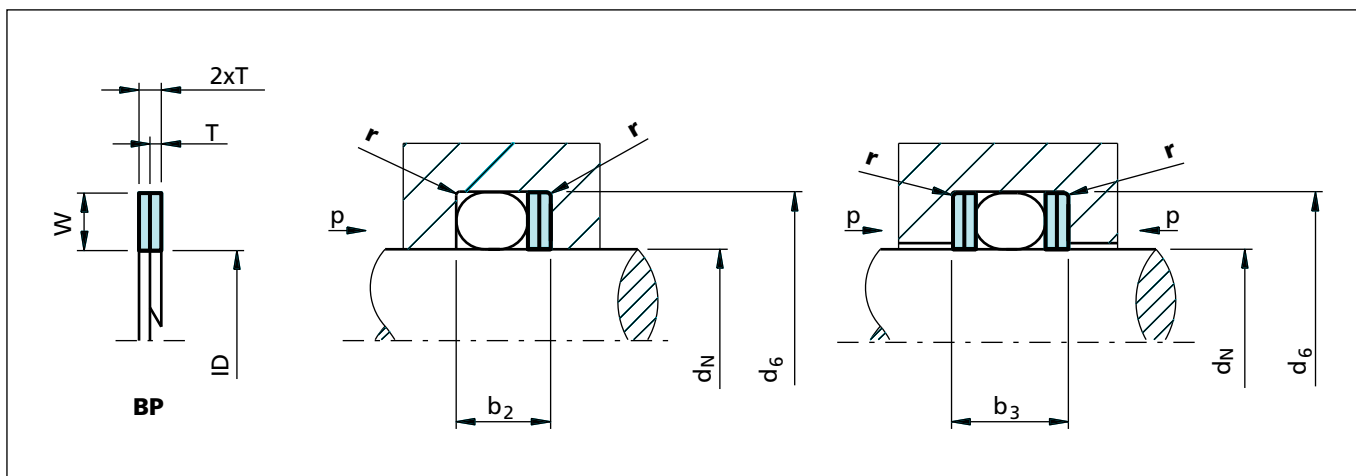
Einbauzeichnung innendichtend, spiralförmige Stützring Bauform
